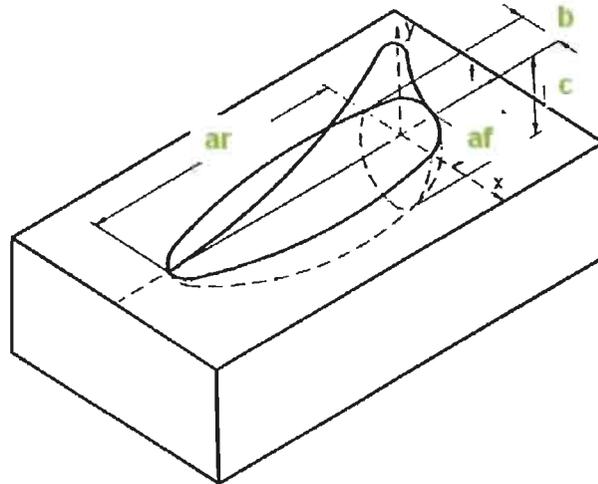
Modelo típico de conductividad, usualmente usado en procesos que involucran depósito de material: (ar) longitud del charco de soldadura, (b) radio del cordón de soldadura, (c) profundidad de la zona afectada por el calor, (d) zona afectada por el calor.
